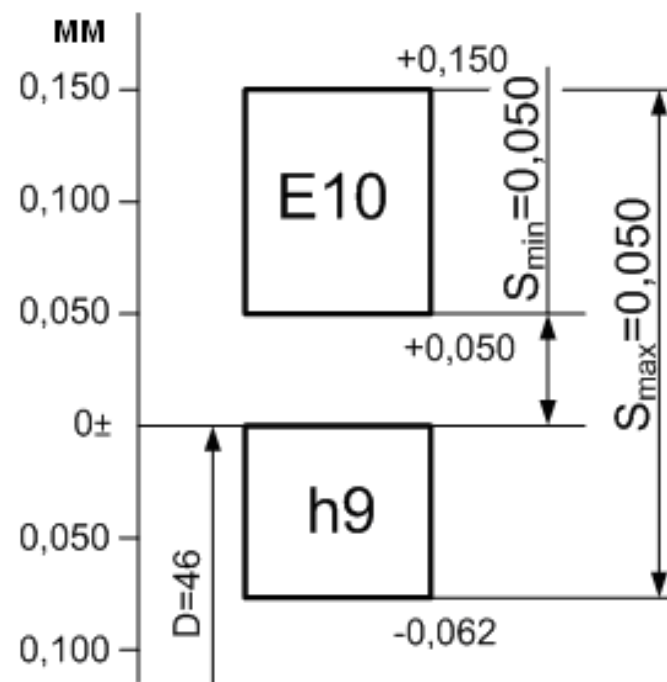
Схема розташування полів допусків деталей з'єднання $\varnothing 46E10/h9$
